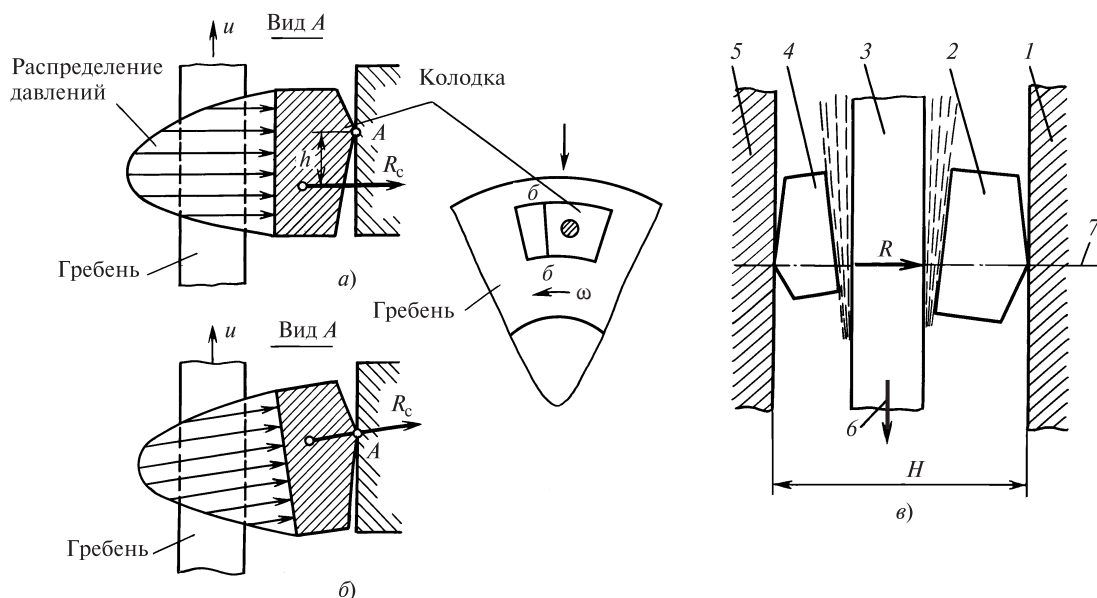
Положение колодок и гребня в упорном подшипнике
